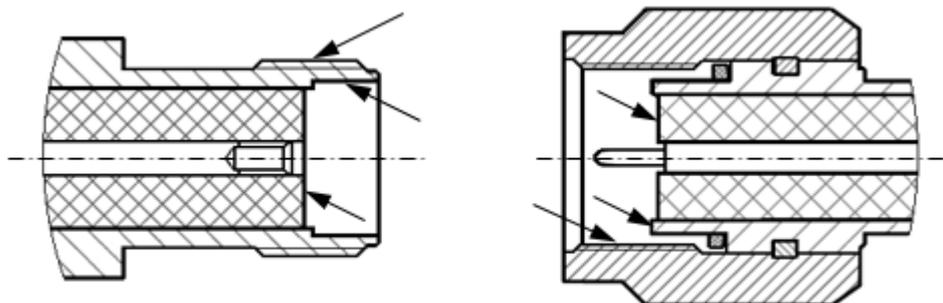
Соединители тип SMA (розетка слева, вилка справа)
